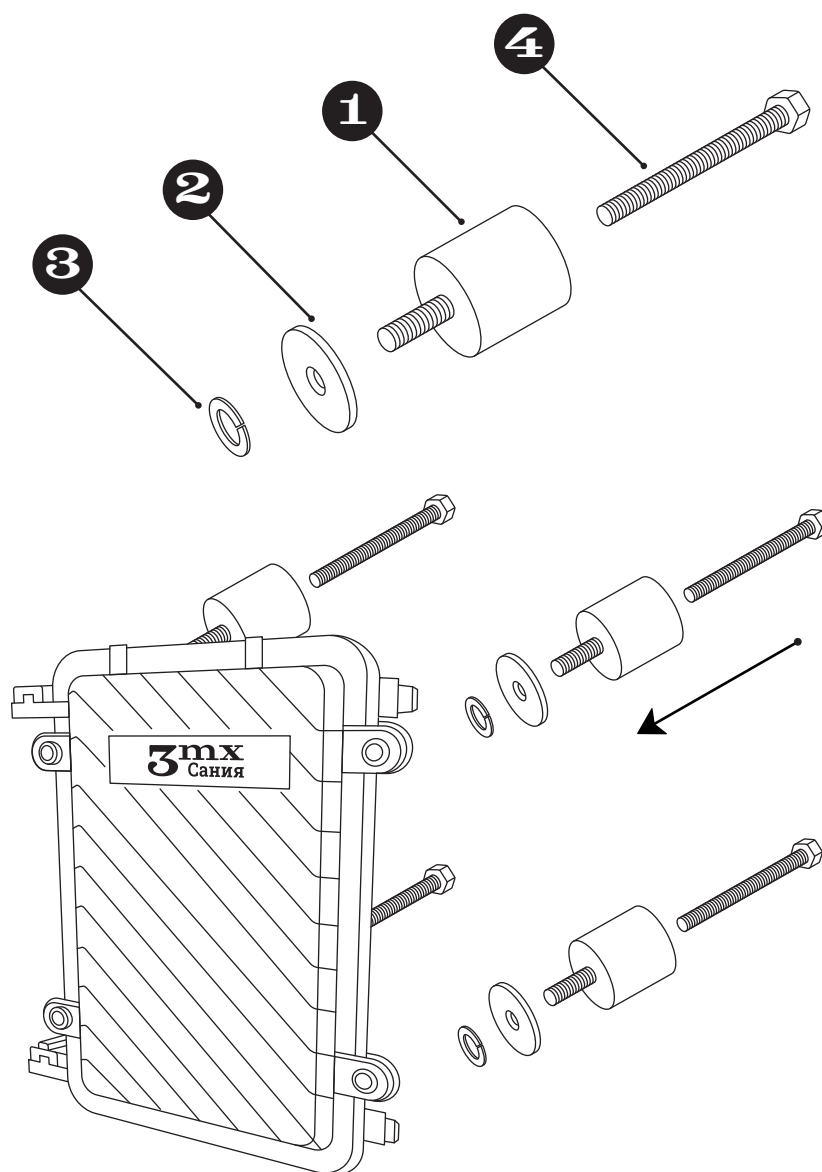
Комплектующие для сборки соединительного крепления детектора
